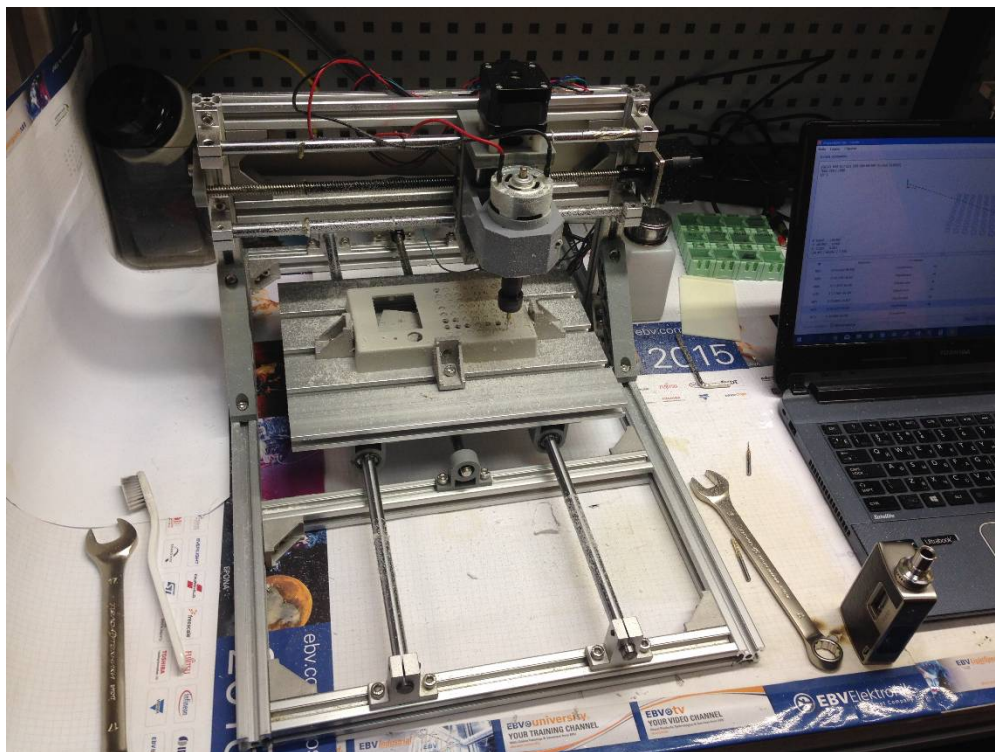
Станок с ЧПУ использованный для изготовления макета корпуса и рабочее место оператора.
